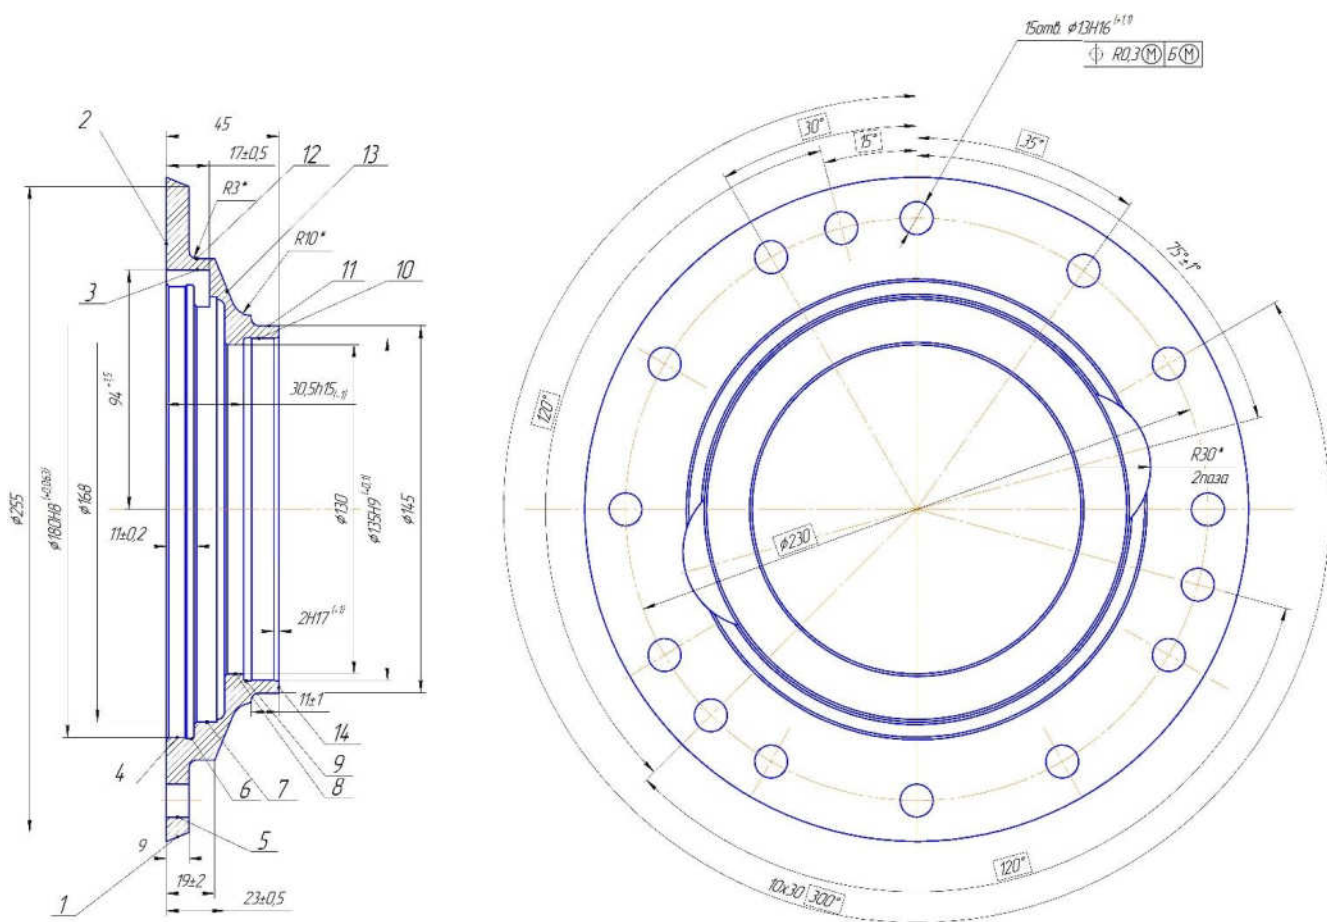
Эскиз детали «Крышка привода главного движения трактора»
